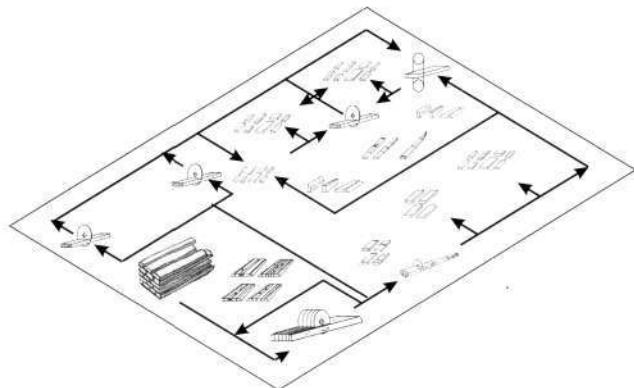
Primjer tehnološkog tijeka u primarnoj pilani za bukvu, uz mogućnost proizvodnje standardnih piljenica i doradnih piljenica za daljnju obradbu u elemente, uključivši tu i popruge
